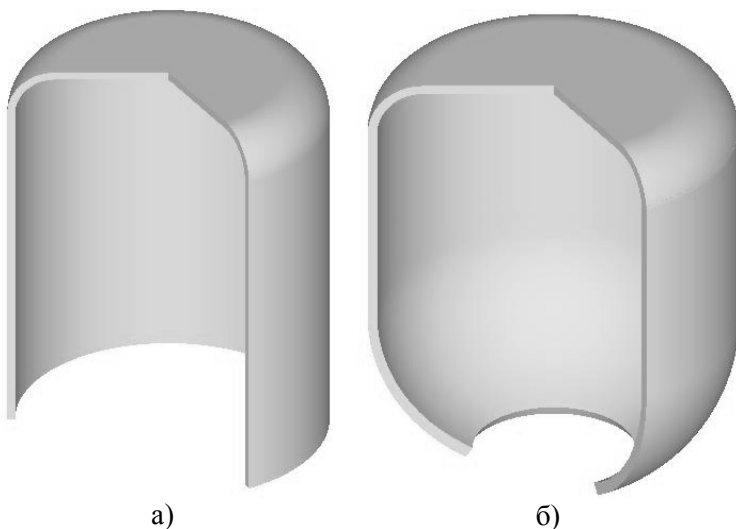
Вихідна заготовка а) в розрізі; б) zdeформована після обтиску
